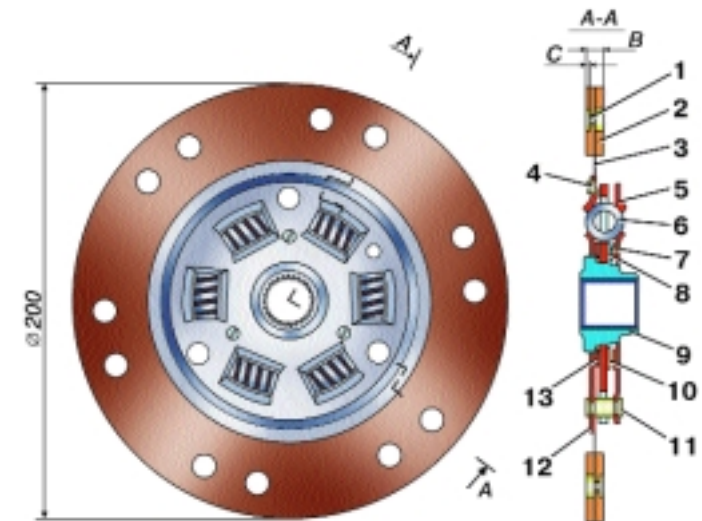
Ведомый диск сцепления «Лук» в сборе: 1 – заклепка крепления фрикционных накладок; 2 – фрикционная накладка; 3 – пружинная пластина; 4 – заклепка; 5 – пластина демпфера; 6 – пружина демпфера; 7 – упорное кольцо демпфера; 8, 13 – фрикционные кольца; 9 – ступица ведомого диска; 10 – пружинное кольцо демпфера; 11 – упорный палец; 12 – ведомый диск; В – размер (7,7±0,3) мм под нагрузкой 509,7 кгс; С – размер не менее 1 мм
